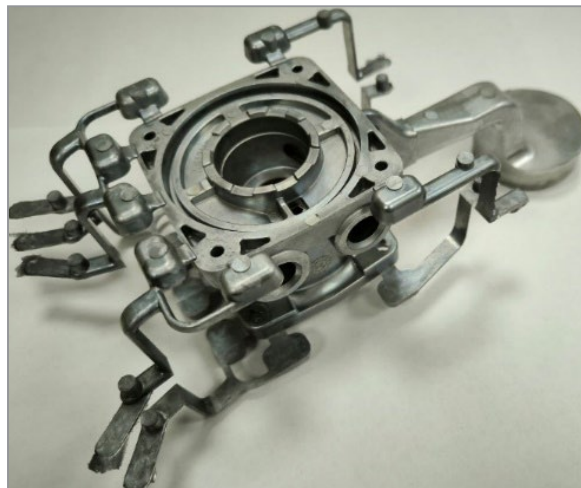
Отливка «Корпус крана тормозного двухконтурного», полученная в пресс-форме с классической вентиляционной системой
